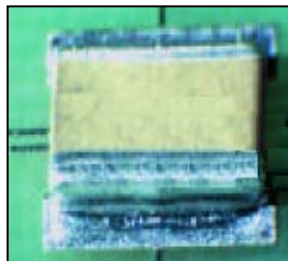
Falla por falta de soldadura en unión.
